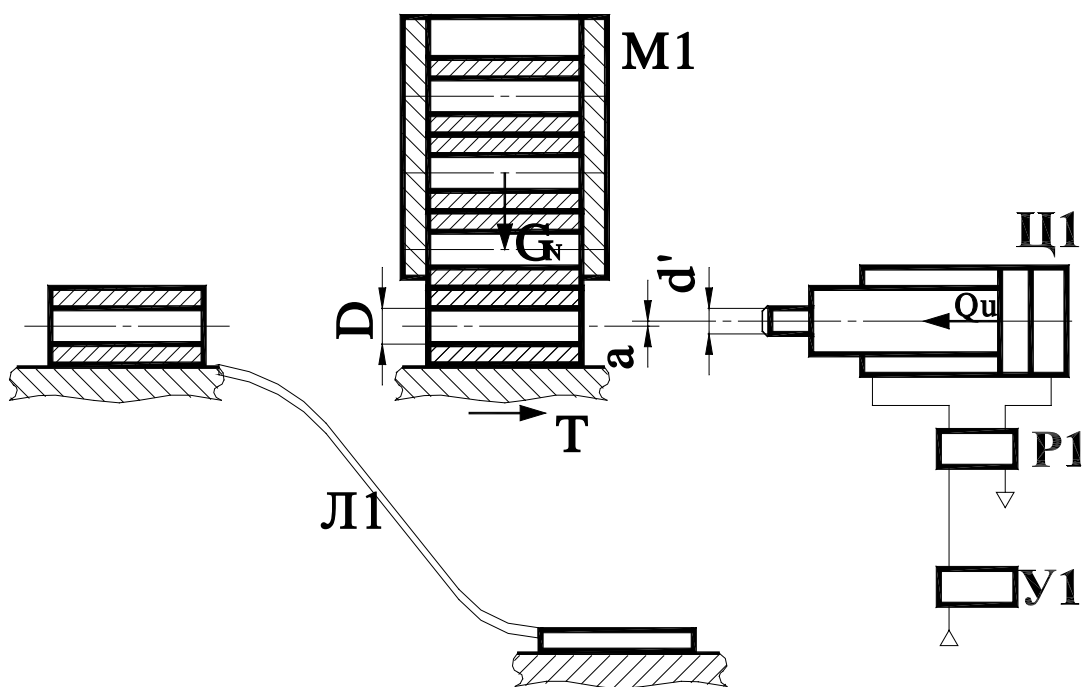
Пневмокинематическая схема лабораторного стенда
